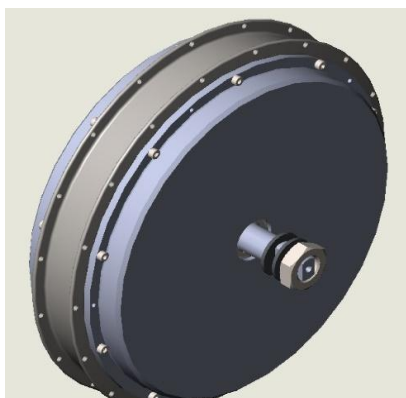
Общий вид мотор-колеса ДБУ-600
